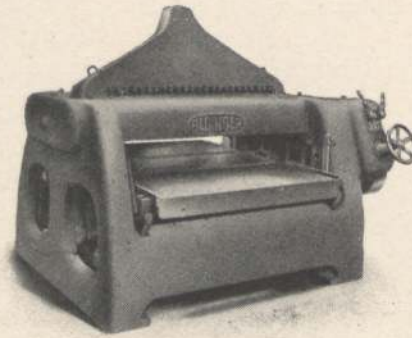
Die Genauigkeits-Hobelmaschine.
